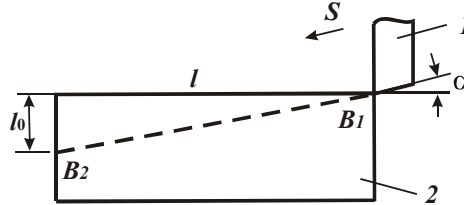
Расчетная схема угла α : 1 – резец; 2 – заготовка.
